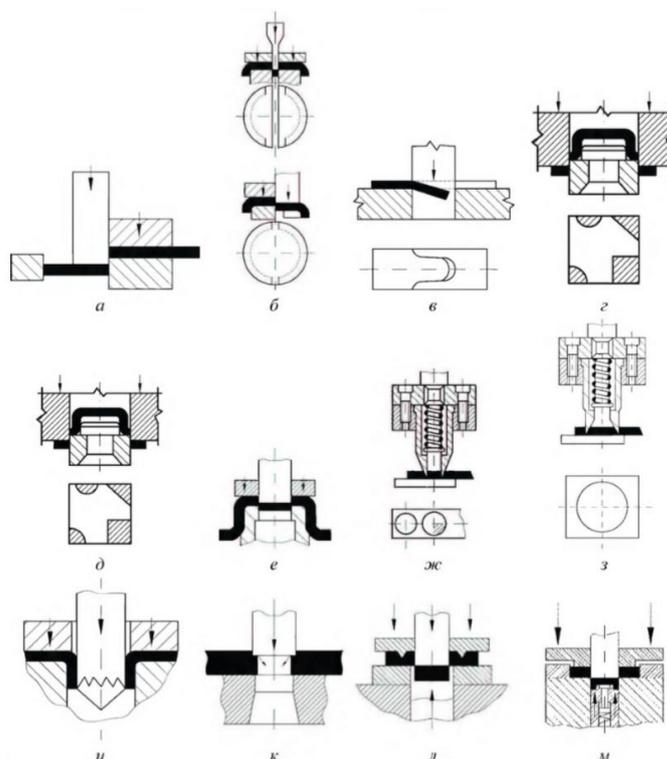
Схемы разделительных операций листовой штамповки: а – отрезка; б – разрезка; в – надрезка; г – обрезка; д – вырубка; е – пробивка; ж – высечка; з – просечка в штампе; и – проколка; к – зачистка; л – чистовая вырубка; м – чистовая пробивка
